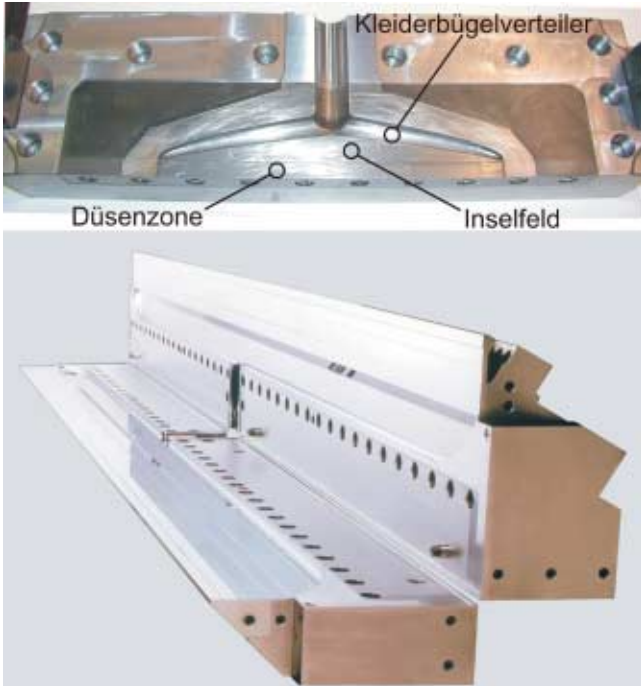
Oben: Werkzeughälfte eines Breitschlitzwerkzeugs mit Kleiderbügelverteiler (Quelle: Institut für Kunststofftechnik Paderborn); unten: T-Verteilerwerkzeug (Quelle: Verbruggen N.V.)
